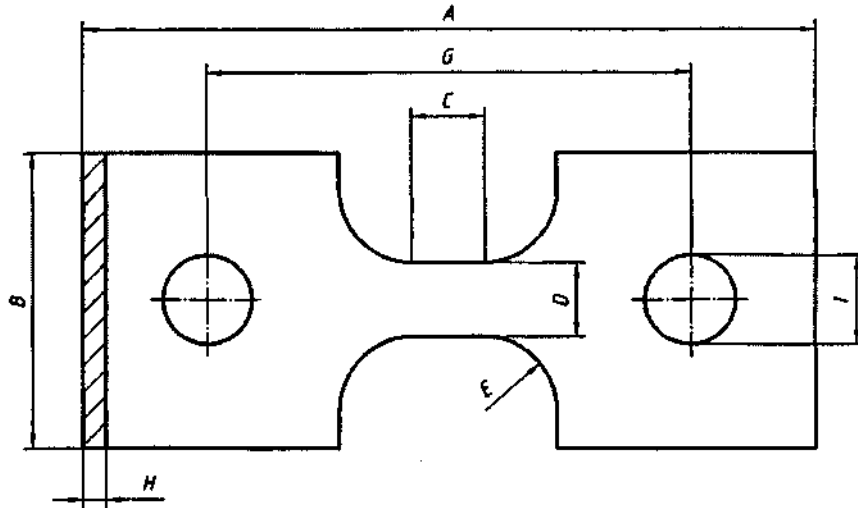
Зразок типу B для випробування на розтяг, виготовлений методом механічної обробки (при $e \geq 25$ мм)
